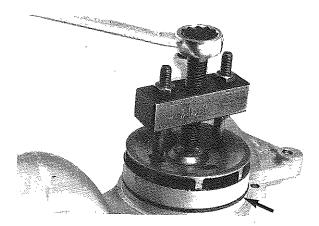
Estrattore n. 29 - Anello di tenuta Puller No. 29 - Seal ring
